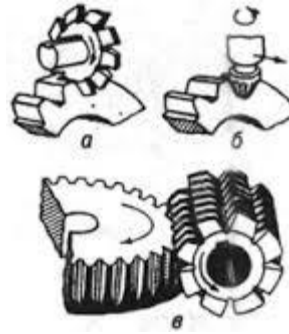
Схема нарезания зубчатых колес методом обката:
